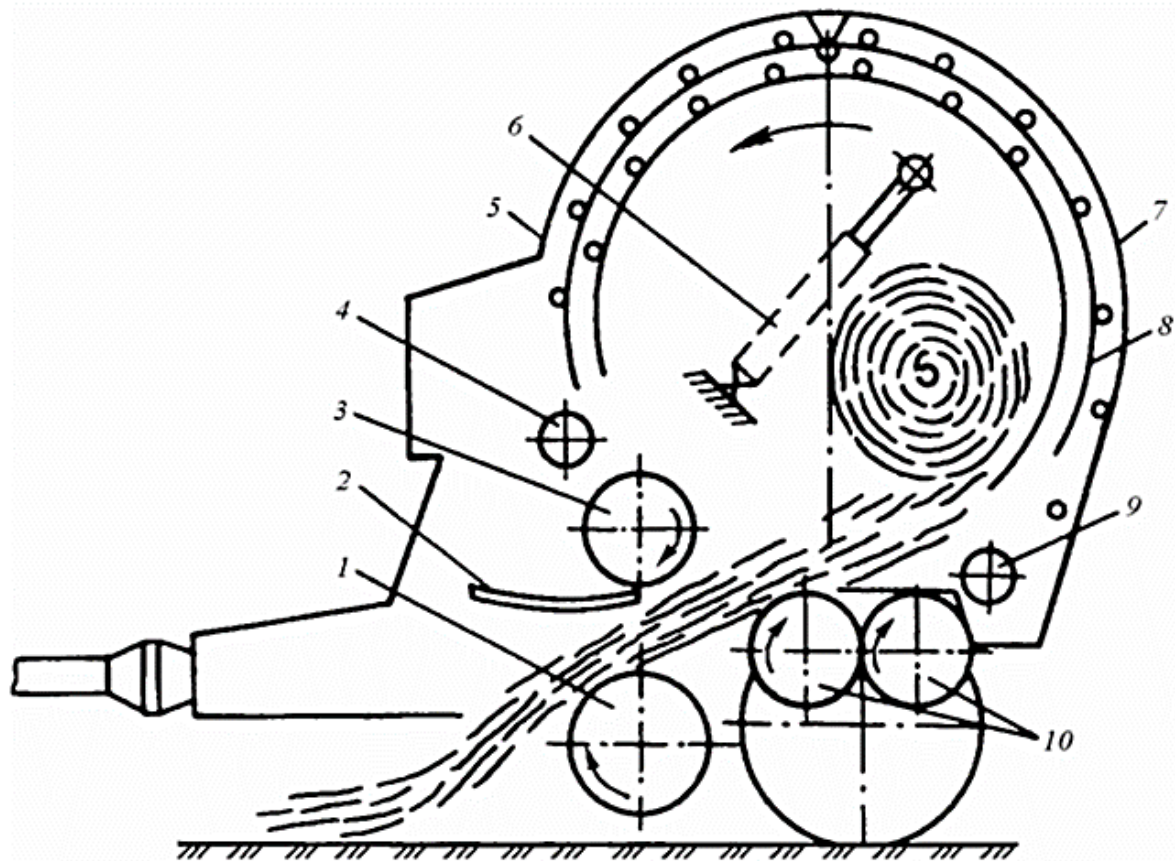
Схема рабочего процесса пресс-подборщика ПР-Ф-750: 1 – барабанный подборщик; 2 – прижимная решетка; 3, 10 – вальцы; 4, 9 – ведущий и ведомый валы механизма прессования; 5, 7 – передняя и задняя части камеры прессования; 6 – гидроцилиндр; 8 – механизм прессования
